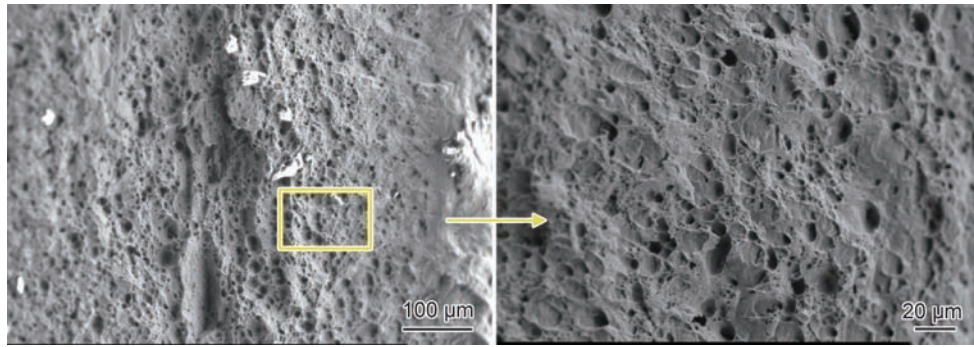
1600-150-0.1 双面焊接断口微观形貌
